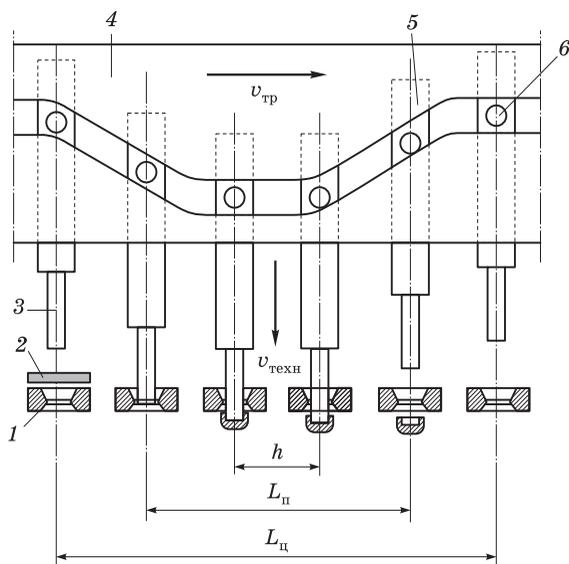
Схематическая развертка прессовой операции на роторной линии:
